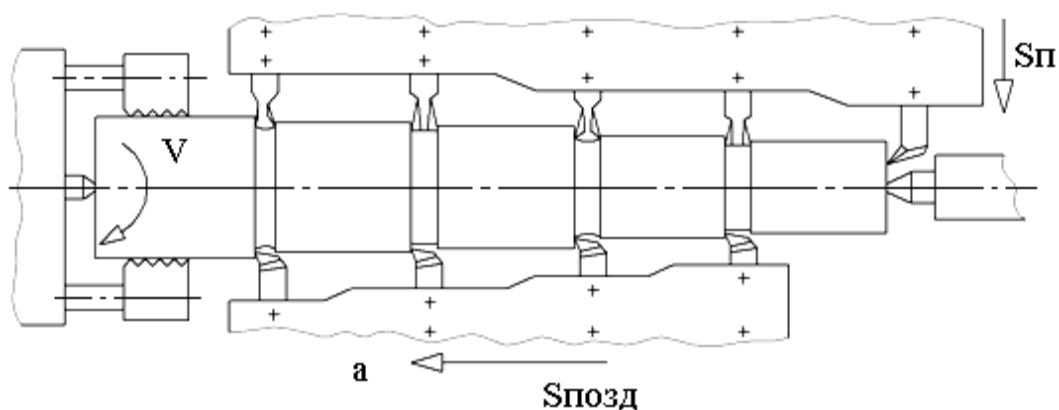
Схеми обробки заготовок на токарному багаторізовому напівавтоматі
